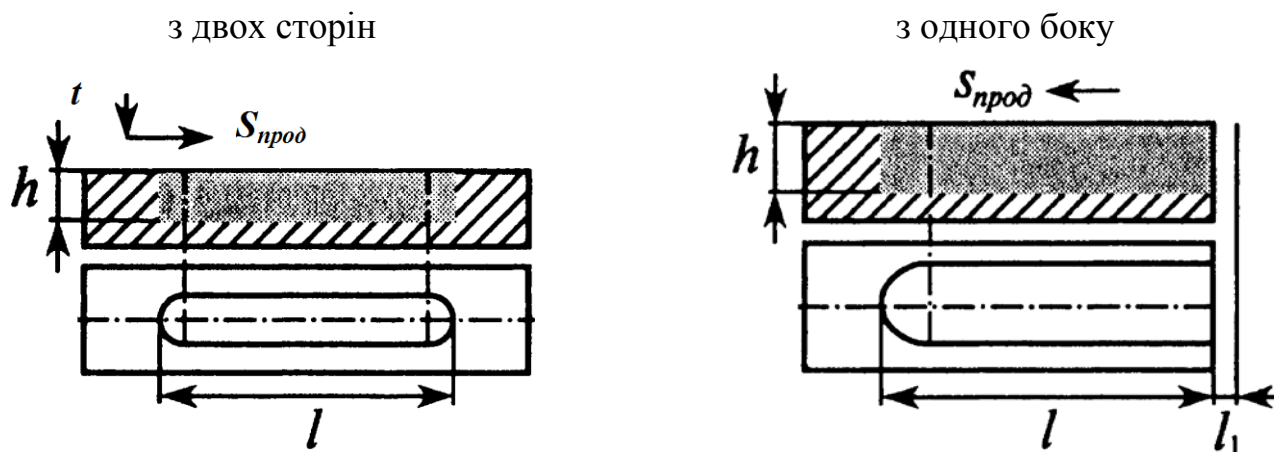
Фрезерування пазів шпонковою фрезою:
